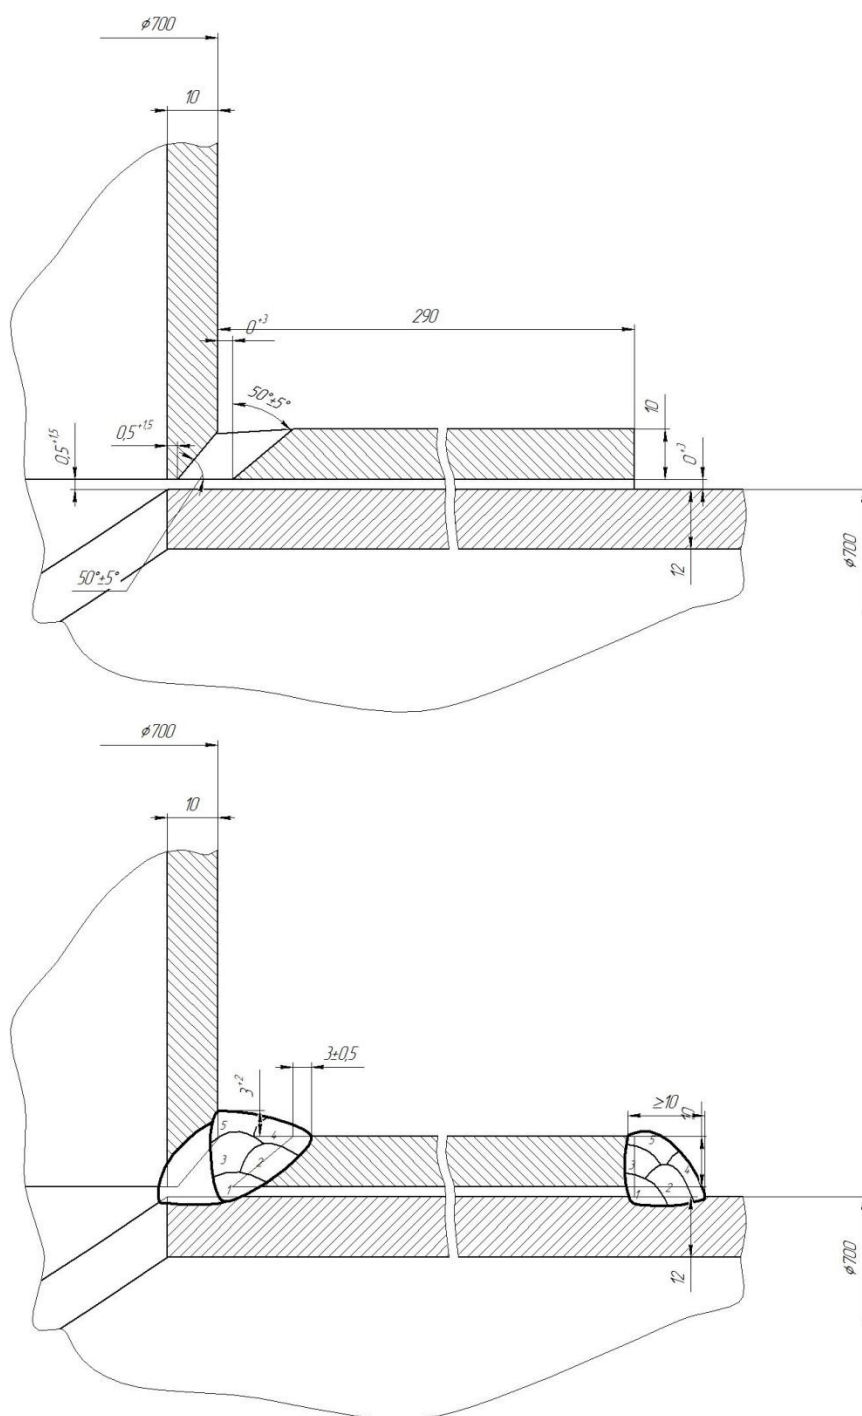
Сборка и сварка тройникового соединения с усиливающей накладкой
